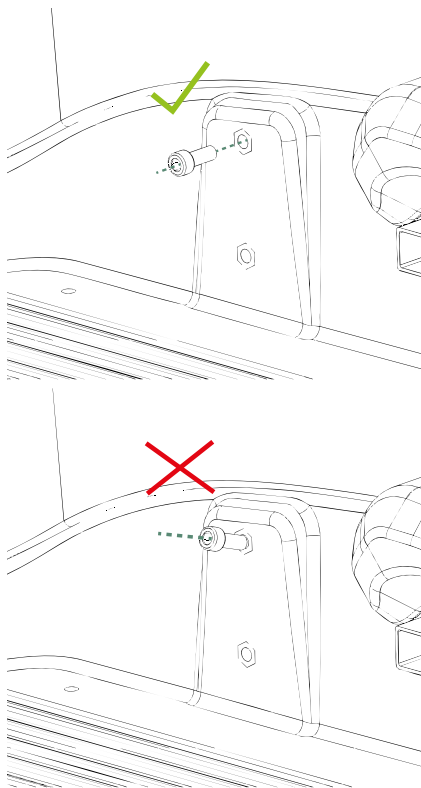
Schrauben immer zuerst gerade von Hand eindrehen.“
